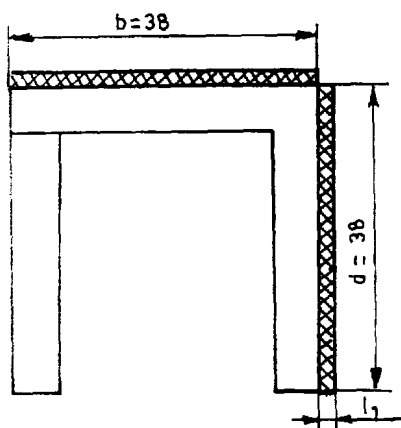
Sección transversal del travesaño: cordones de soldadura.
